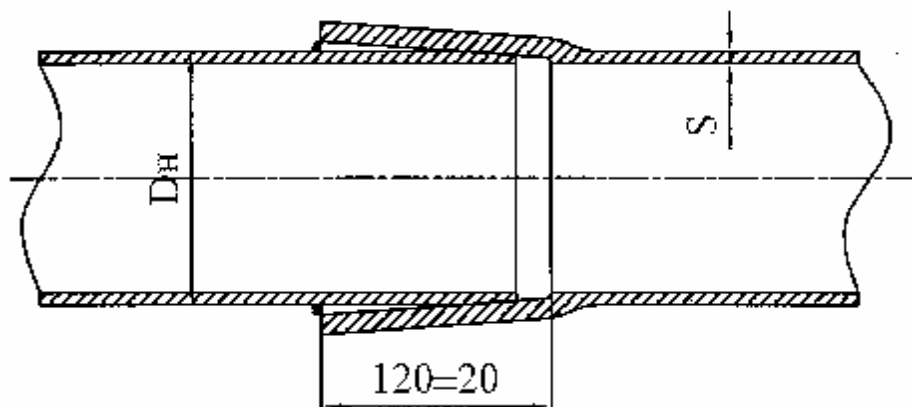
П2. Схема сварного нахлестного соединения
